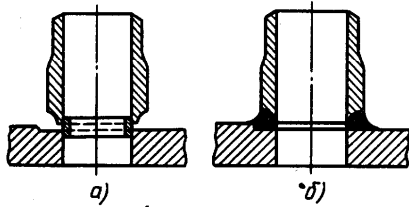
Сварка штуцера с использованием подкладного кольца
